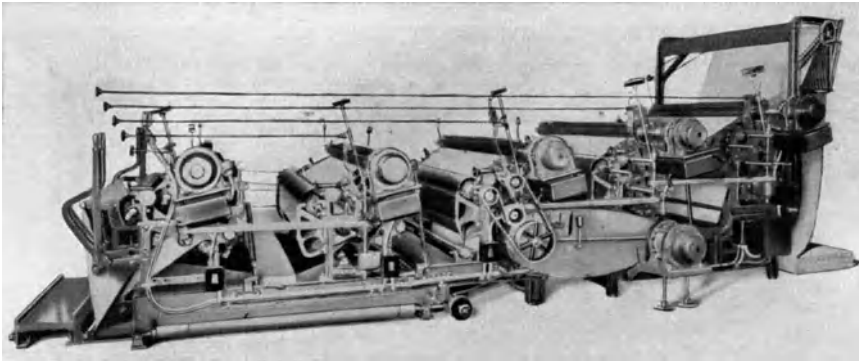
Fünfzylinder-Schermaschine. (Parks & Woolson Machine Company. Springfield, Vermont.)
